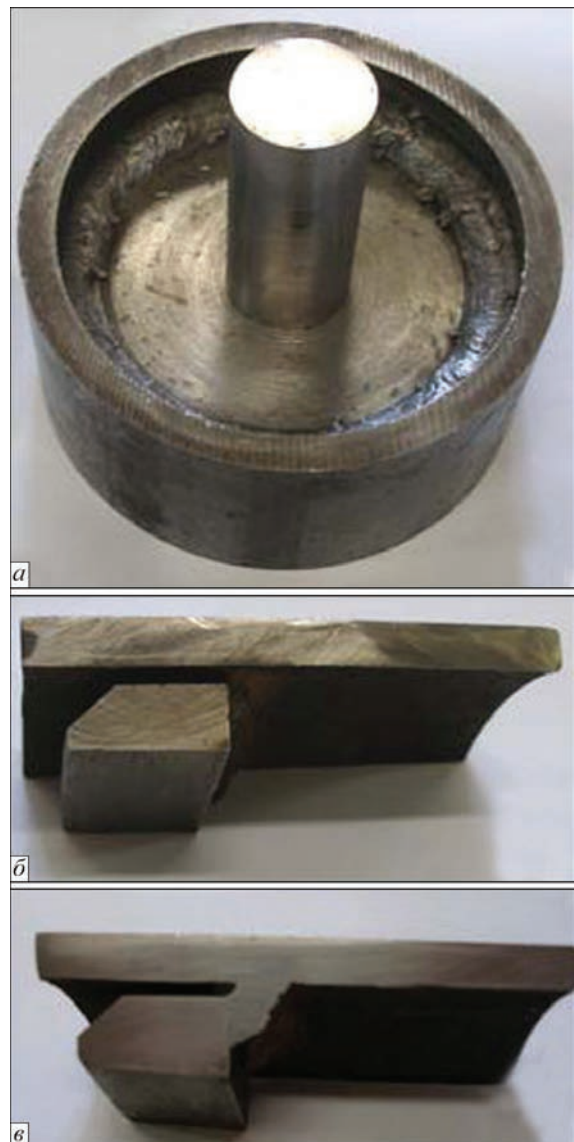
Результаты приварки доньшка к внутренней поверхности трубы: а — кольцевой шов с перекрытием; б — реальный зазор между доньшком и трубой; в — форма сварного соединения
